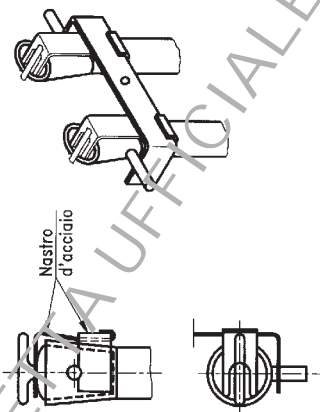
Fissaggio della protezione a molla d'acciaio
